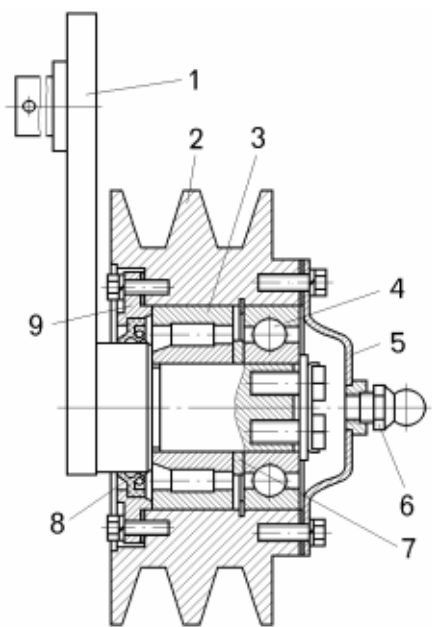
Натяжной ролик с рычагом в сборе:
